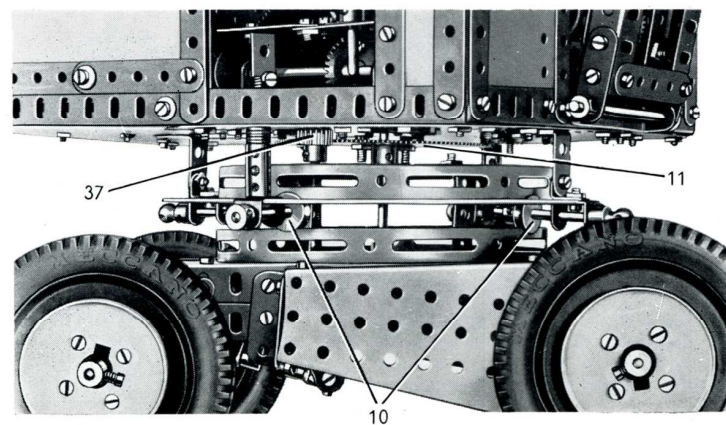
Vue de détail du roulement à galets monté sur la base mobile
